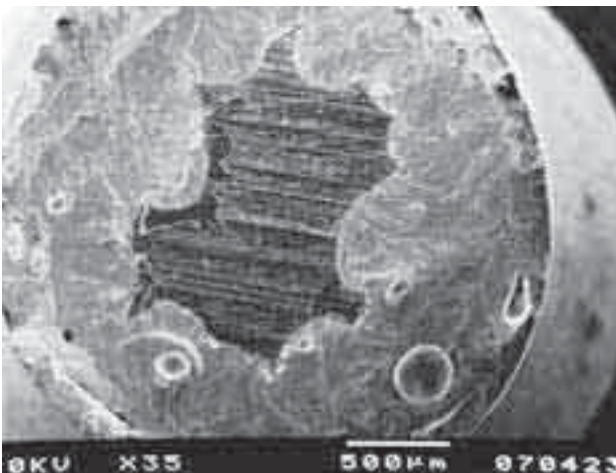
MEV da fratura do corpo-de-prova na condição soldado a laser, mostrando a solda com porosidades e a região central com falha de soldagem; 35X
